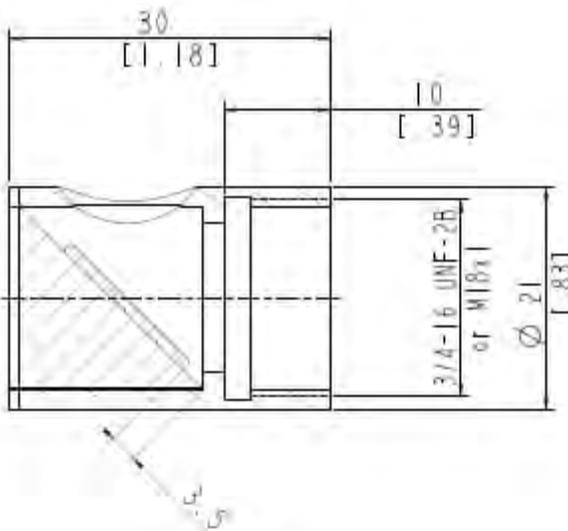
Dimensions du miroir pour visée d'angle 90° (XXXMI3100RAM)
